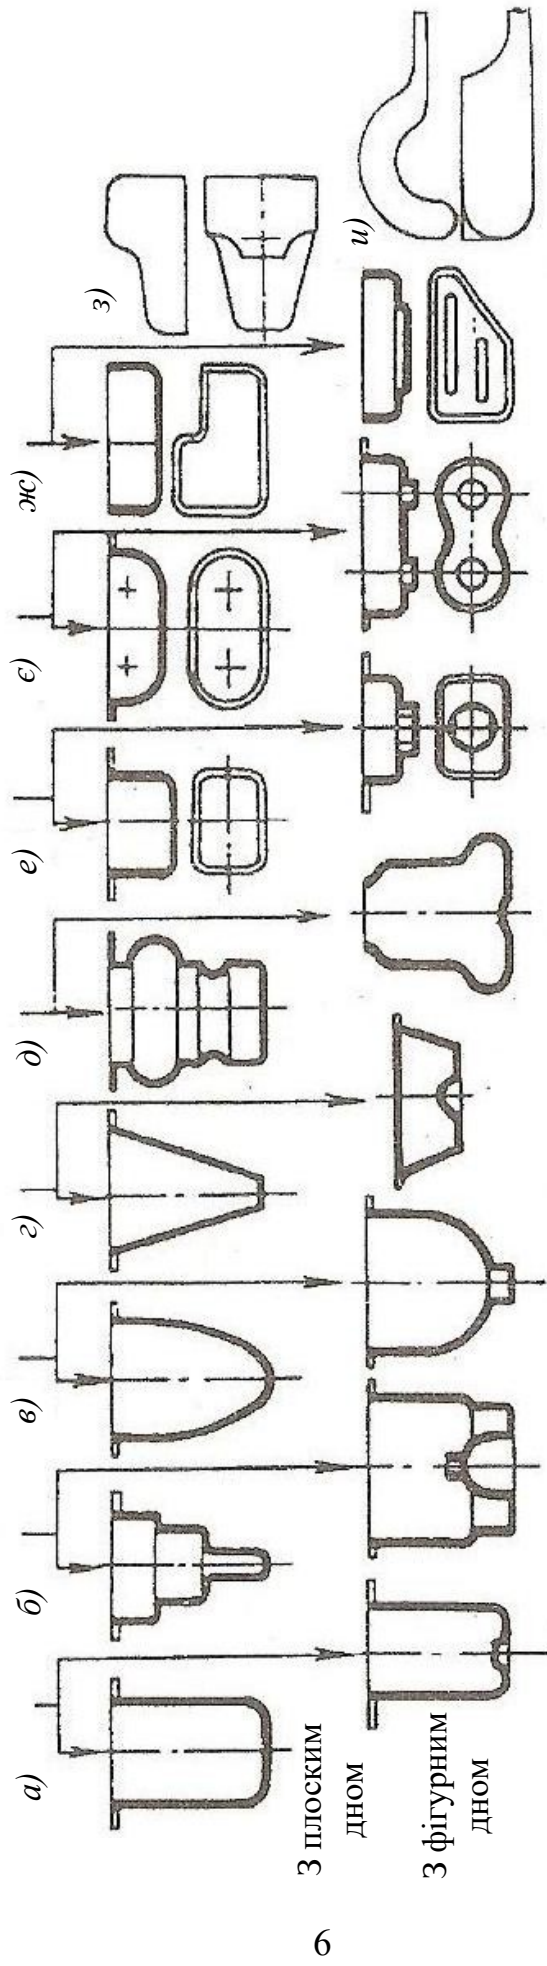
Порожністі деталі різної форми, виготовлені витягуванням
